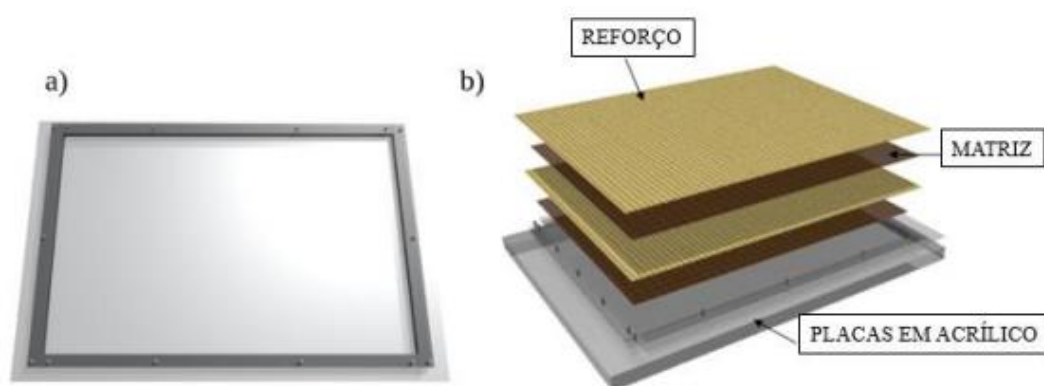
Molde utilizado para a confecção dos compósitos; e b) esquema de moldagem (Trindade, 2017).
